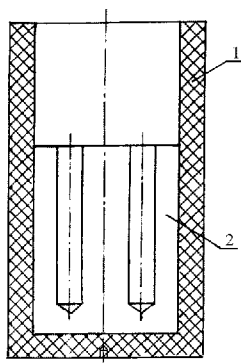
Тигель-форма для получения литых заготовок в модернизированной печи на базе установки ОКБ-860:
